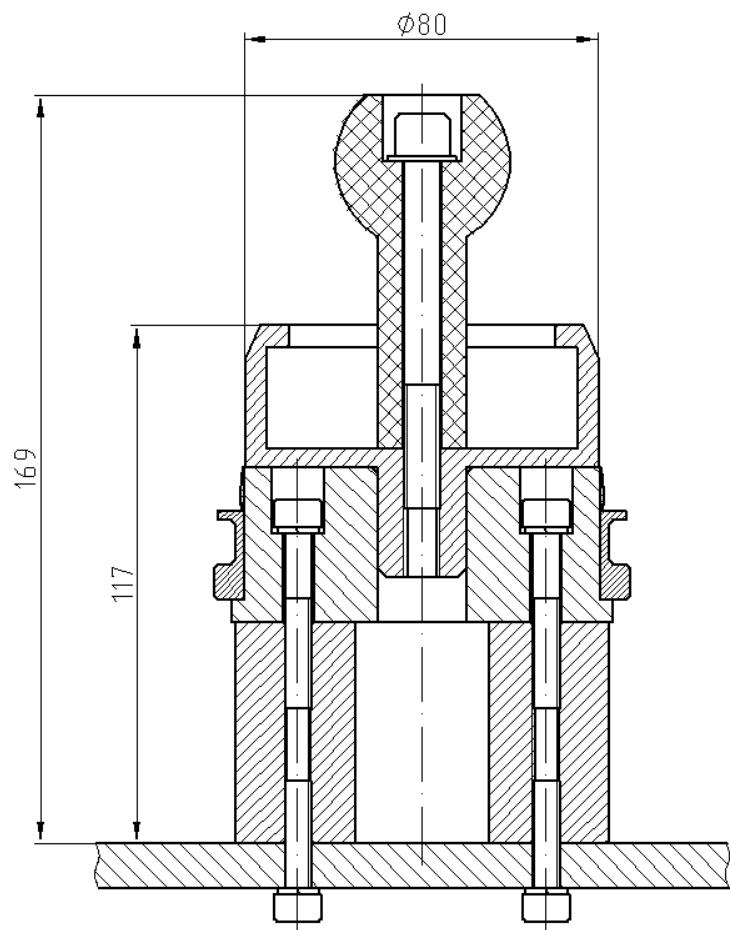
ЗМ 7820-4733, Приспособление для установки сальникодержателя с сальником без пружины
